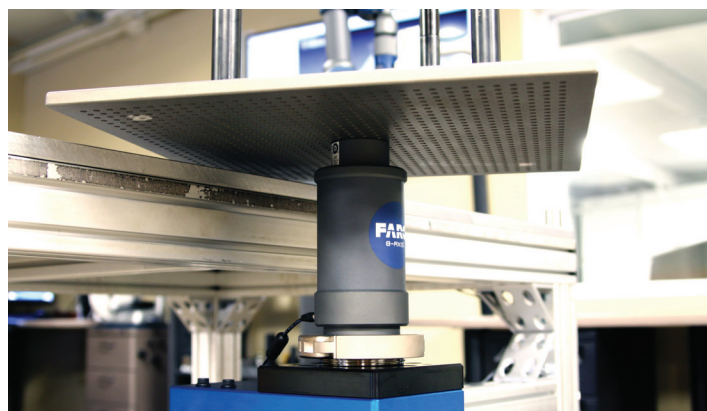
A Diverse Dimensions criou seu próprio suporte para o 8-Axis
